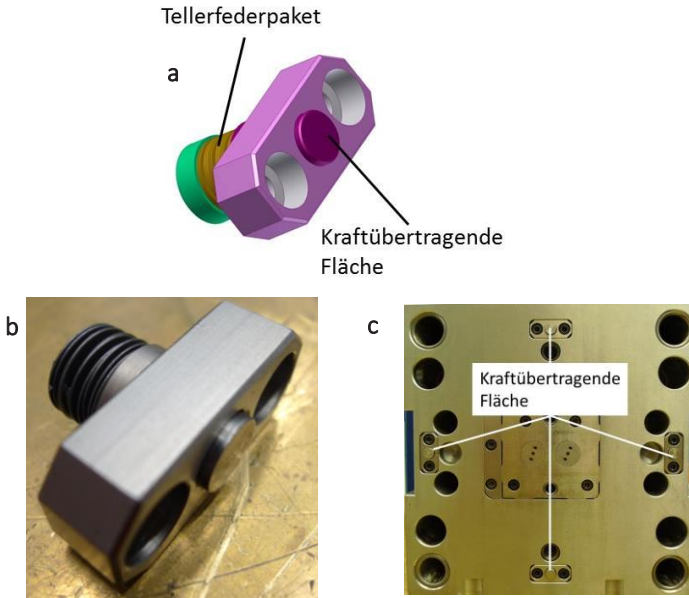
Darstellung der Tellerfederpakete für die Gewährleistung einer definierten Werkzeugöffnungs-bewegung: a Schematisch im 3D-CAD, b Aufnahme eines Federpaketes, c Aufnahme der Auswerferseitigen Werkzeugplatte mit den eingebauten Federpaketen
